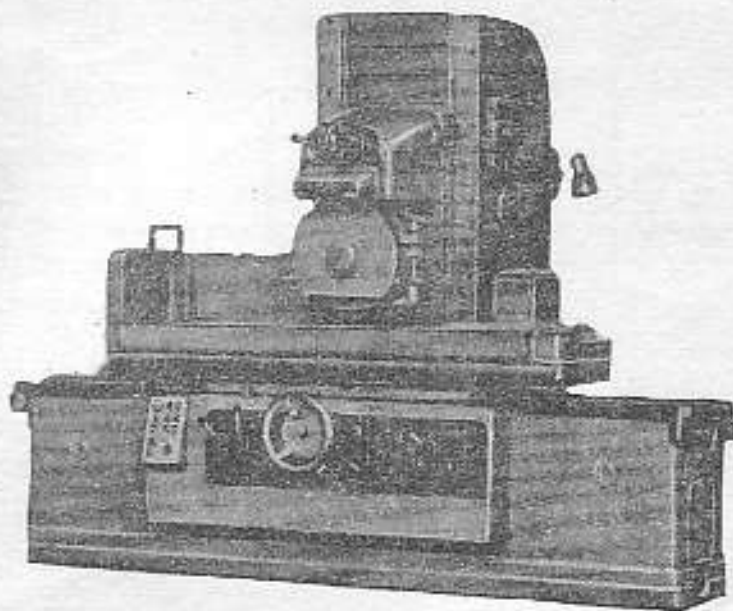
Рис. I. Продольно-шлифовальный станок, модель 3Б722
